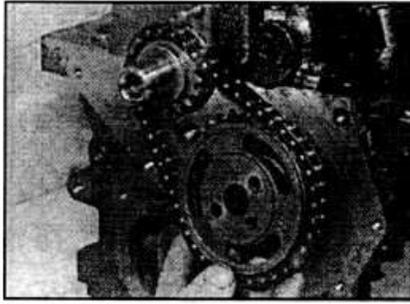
А.19. Установка цепи на коленчатый вал и звездочку распределительного вала.
